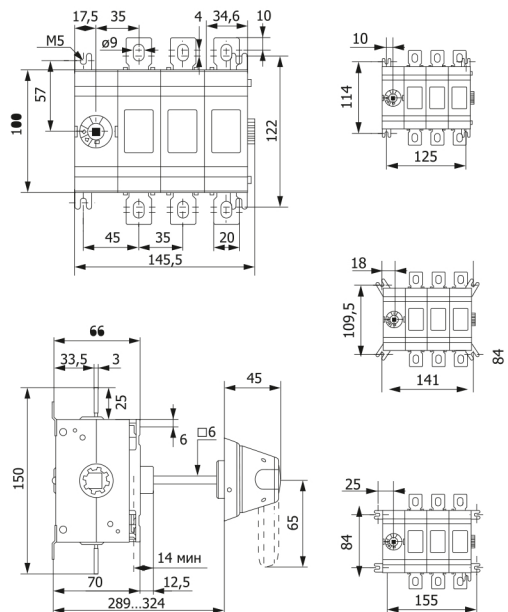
Габаритные и установочные размеры рубильников 160-250А
